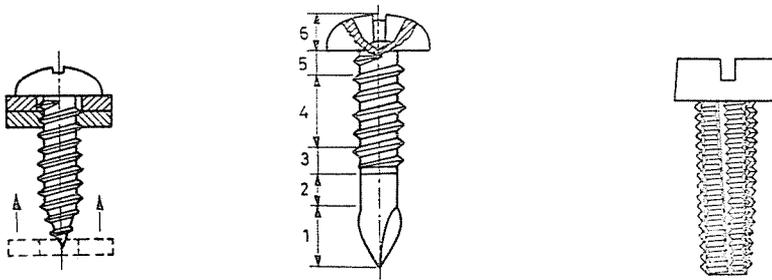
Blechschraube Abb. 9. Selbstschneideschraube Abb. 10. Gewindefschneideschraube
